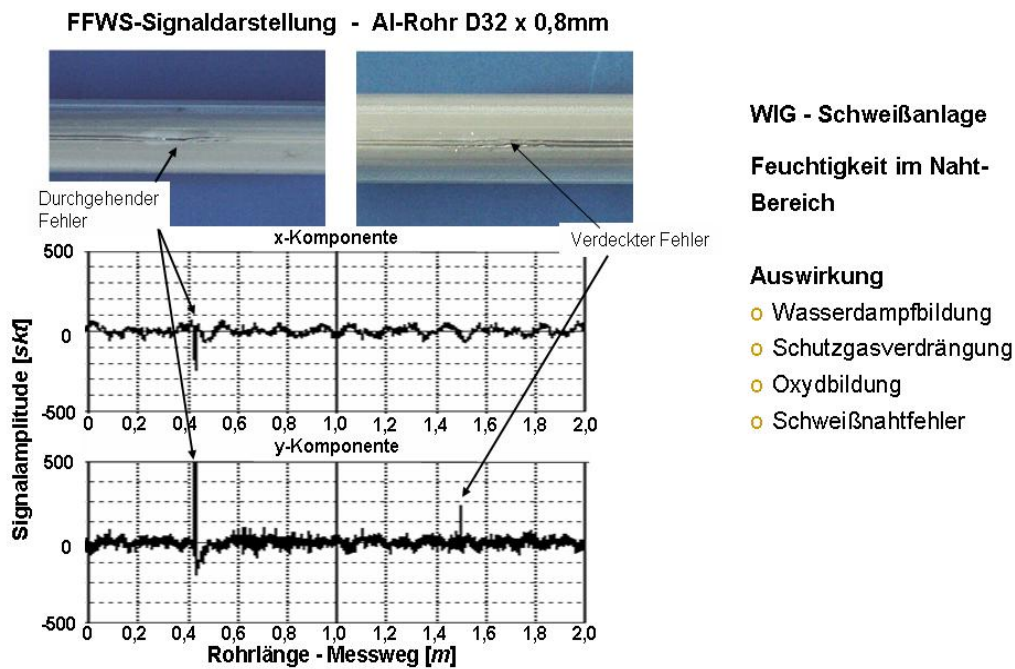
WIG-Schweißnaht mit Bindefehlern
